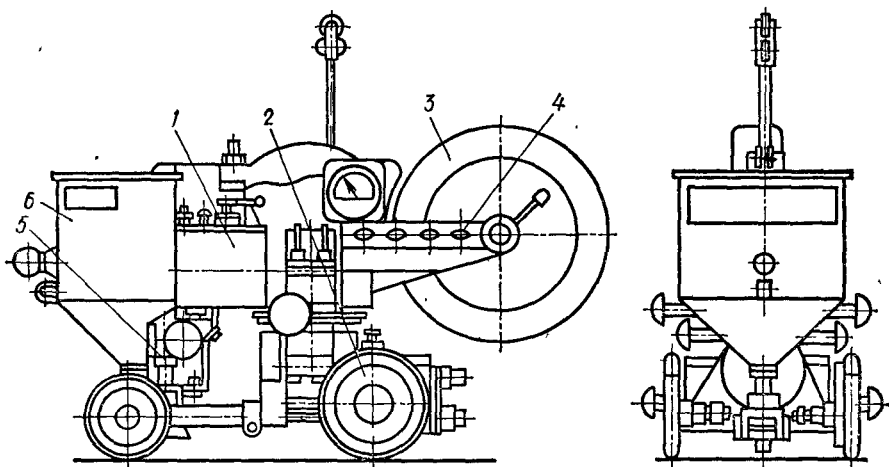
Общий вид сварочного трактора ТС-35
